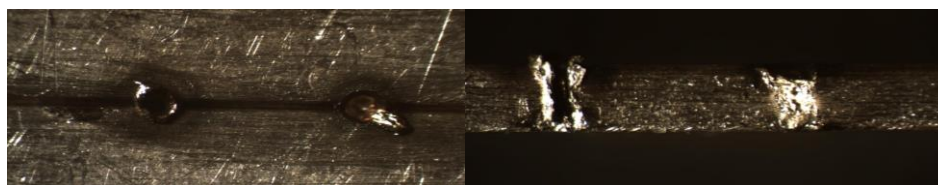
Сварка с добавлением Al+CuO
